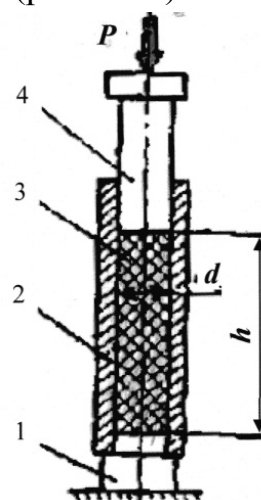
Схема прессования ВВ в корпус боеприпаса:
